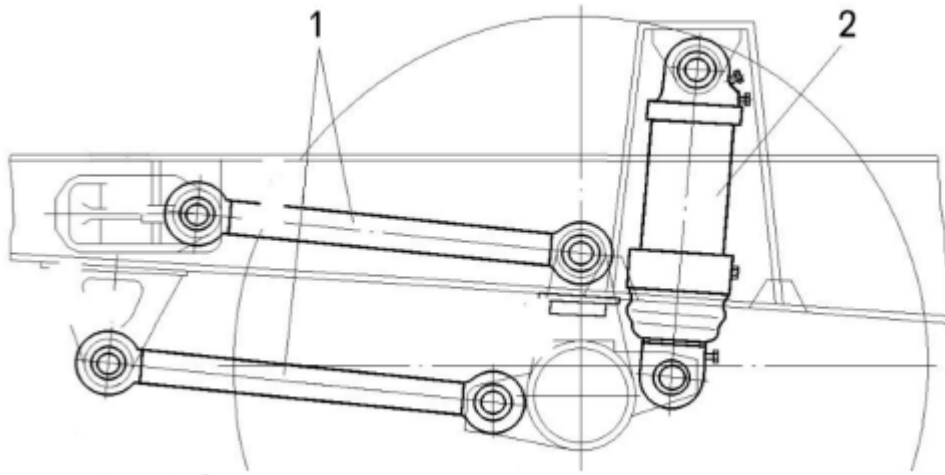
Схема крепления гидроцилиндра и рычагов подвески
